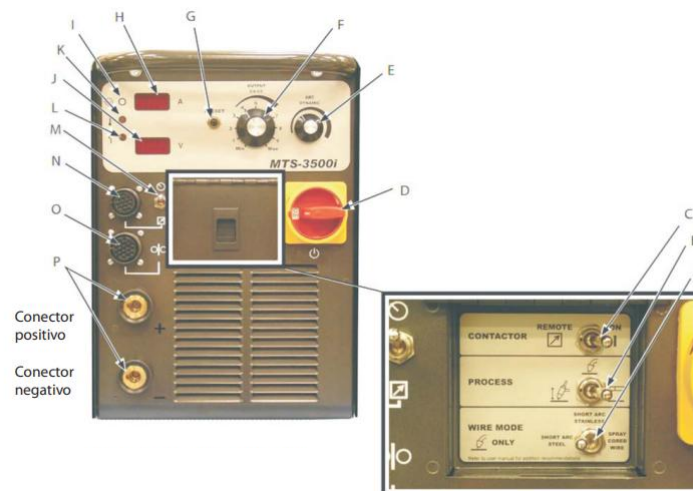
Máquina de Soldagem MTS-3500i – Controles e Indicadores - Fonte: Manual Eutectic Castolin
